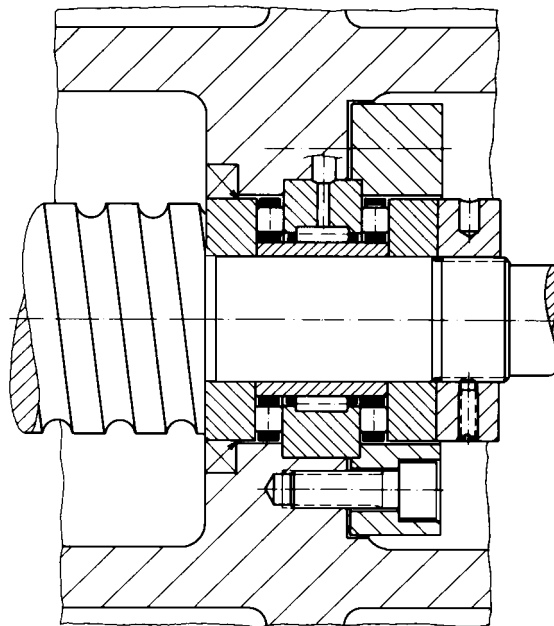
Einbaubeispiel für kombiniertes Radial-Axial-Rollenlager für eine Kugelumlaufspindel
